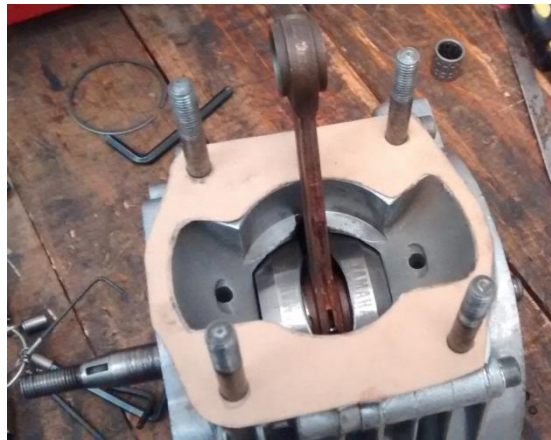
Montaje conjunto cigüeñal-biela lubricado
